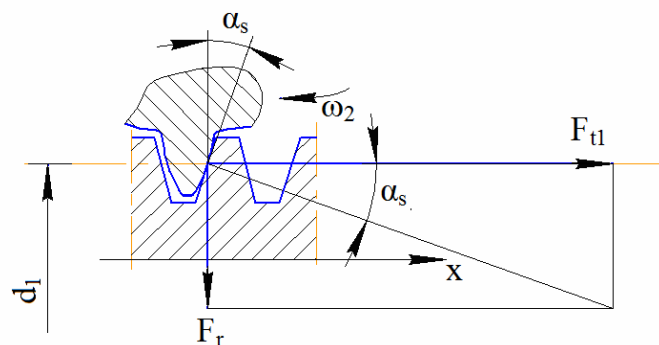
Переріз, перпендикулярний до вісі черв'ячного колеса і який проходить через вісь черв'яка
